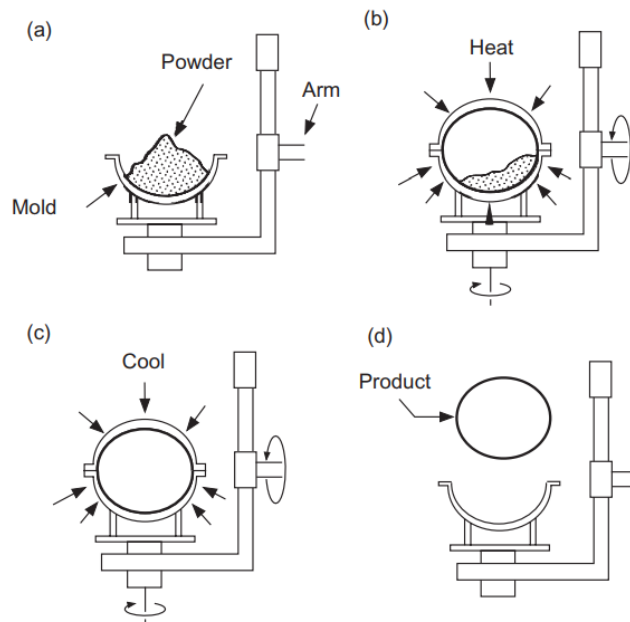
Forma a pec pro rotomoulding <sup>[46]</sup>
